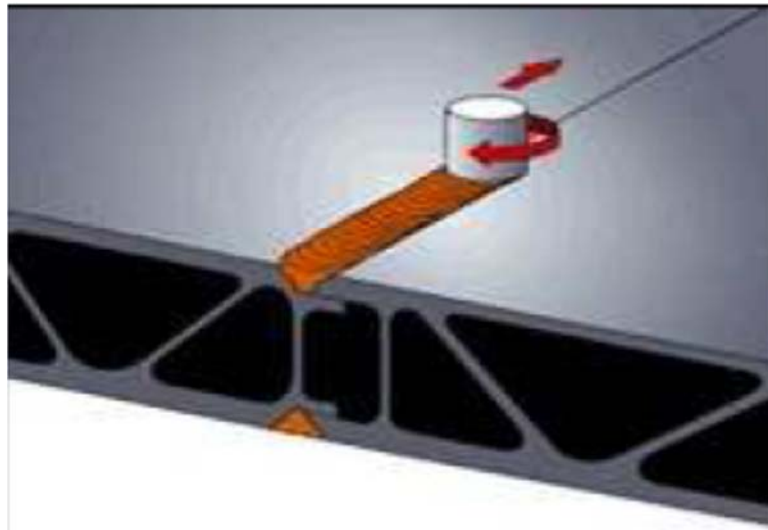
Assemblage de l'avion Eclipse avec le procédé de FSW. [2.8].
